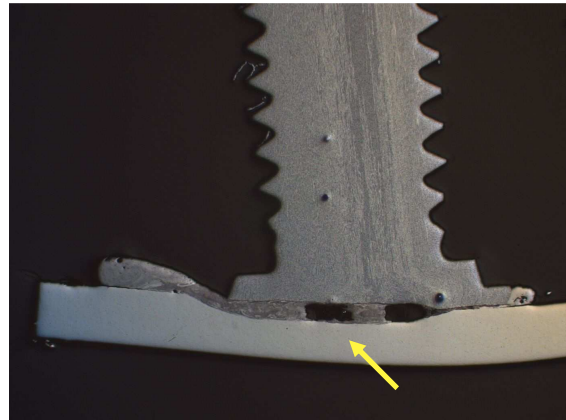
erhöhter Abbrand beim Schweißprozess
